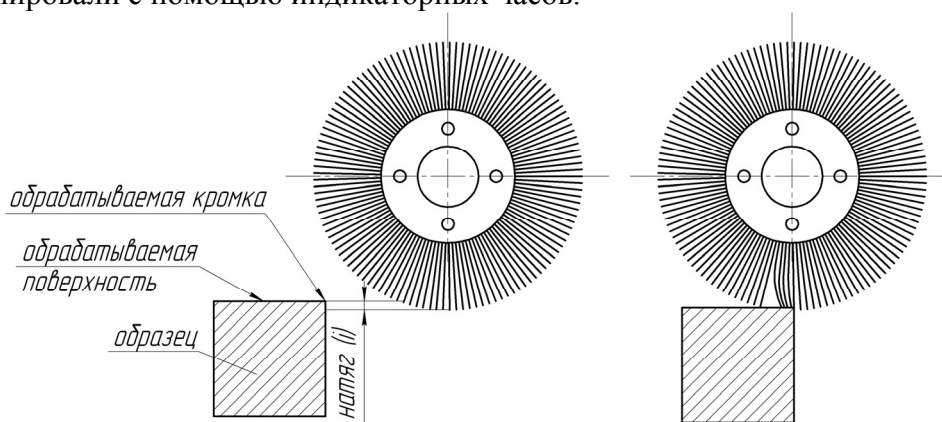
Схема установки натяга перед обработкой дисковым ПА инструментом.
